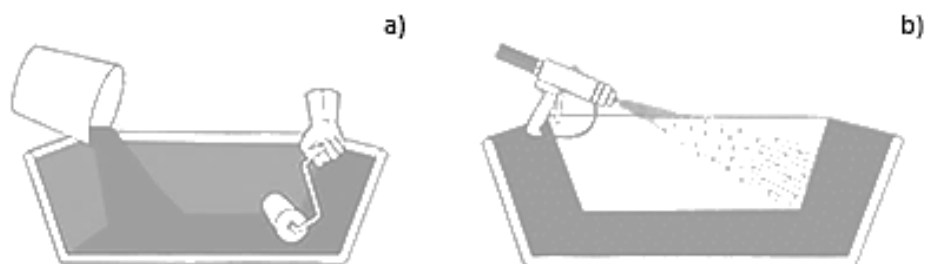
Técnicas de fabrico de moldação por contacto a) Deposição Manual, b) Moldação por Projeção [65]
